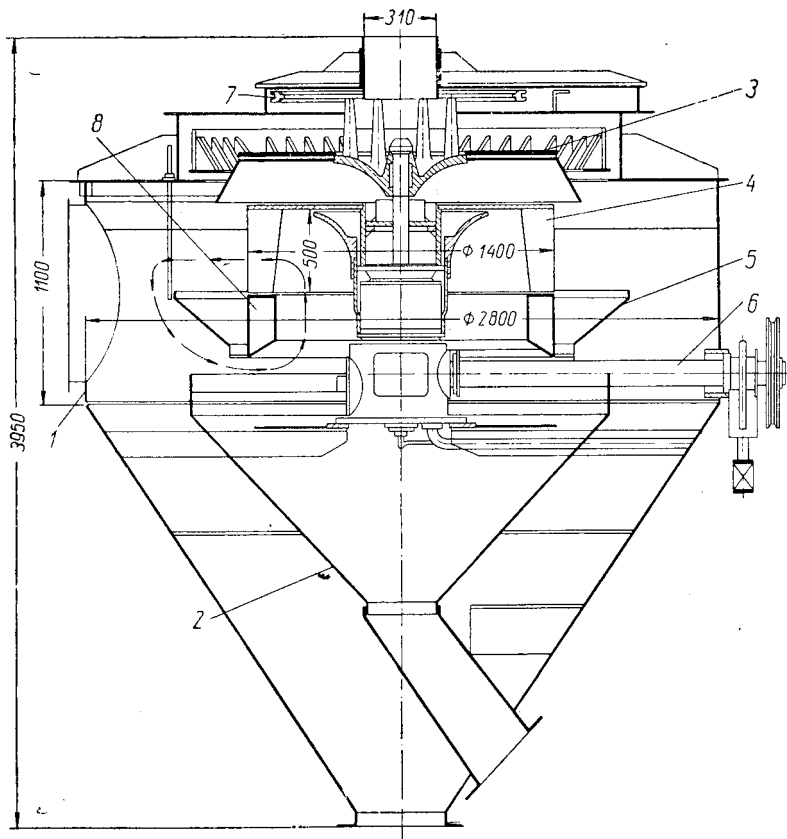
Центробежный воздушный сепаратор ВСФ 1100/2600
